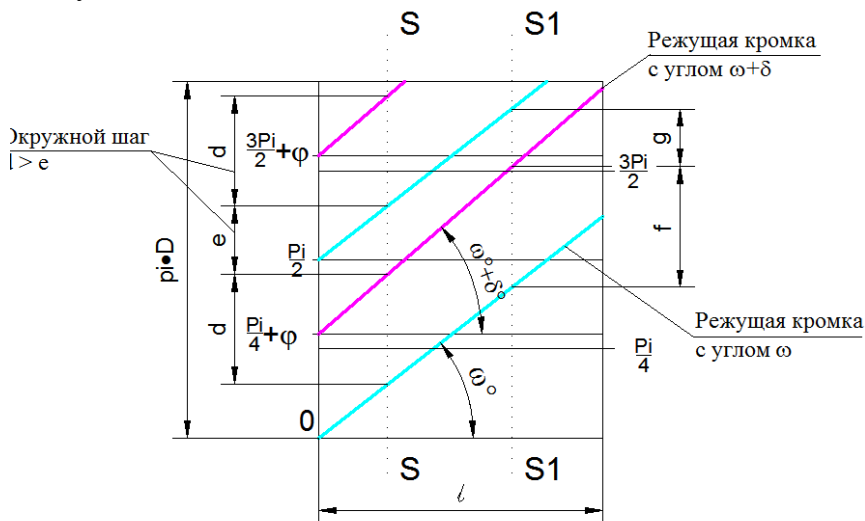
Развертка рабочей части концевой фрезы с модернизированной режущей кромкой
